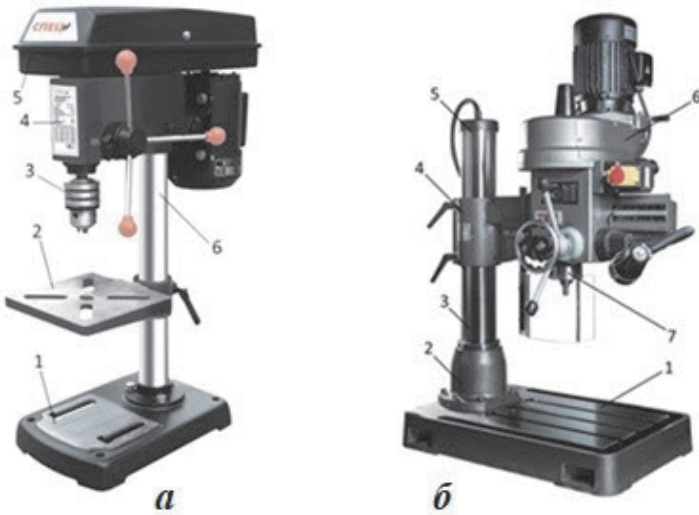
Свердлильні верстати: а — вертикально-свердлильний верстат: 1 — основа, 2 — стіп, 3 — шпиндельний вузол, 4 — направляючий кронштейн, 5 — коробка швидкостей, 6 — колона; б — радіально-свердлильний верстат: 1 — основа, 2 — нерухома колона, 3 — обертова колона, 4 — траверса, 5 — механізм підйому і опускання траверси, 6 — свердлильна головка, 7 — шпиндель
